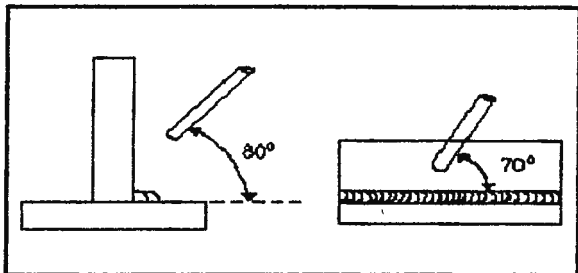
Todas las pasadas apoyadas en la placa horizontal
